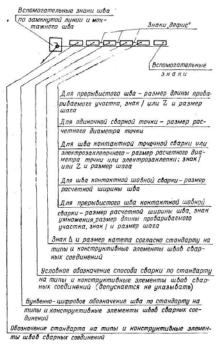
Схема структуры условного обозначения стандартного шва или одиночной сварной точки
